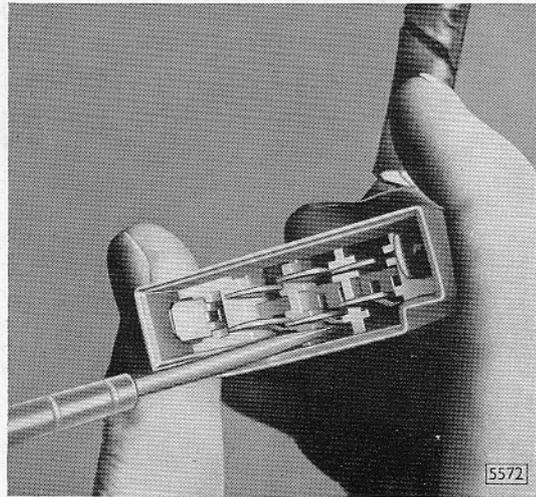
Mit dünnem Schraubenzieher Steckerzungen einzeln beidrücken und Kabel für Kabelsatz Signalschalter aus Gehäuse herausziehen
